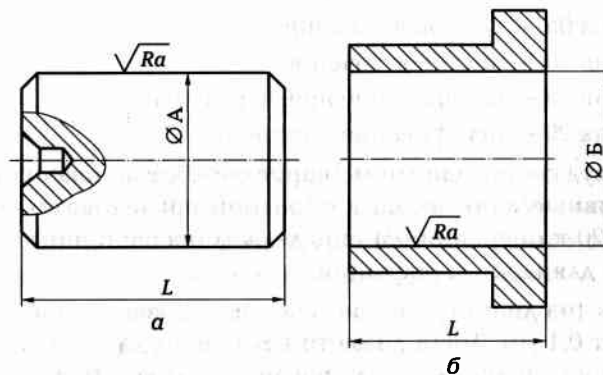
Эскизы детали — вал (а) и детали — втулка (б)
